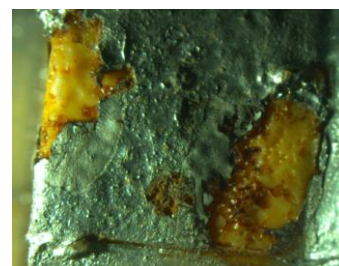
Pormenor do interruptor de poliestireno onde é visível a superfície degradada por baixo da zona de colagem.
